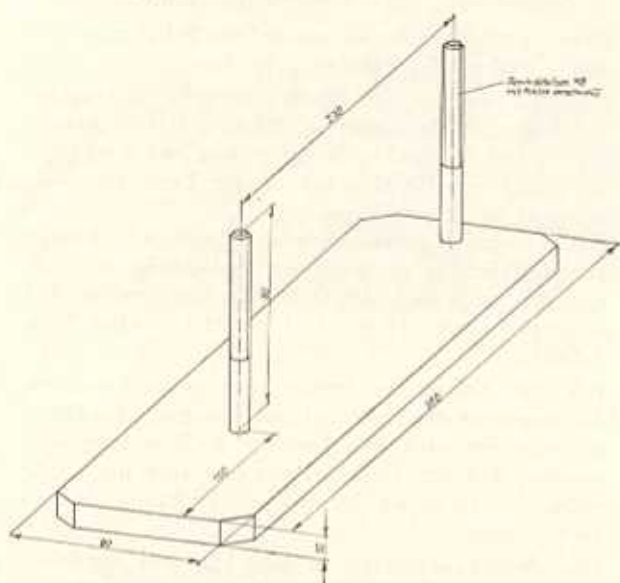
Haltevorrichtung für Lenkgetriebe (Maßskizze)
